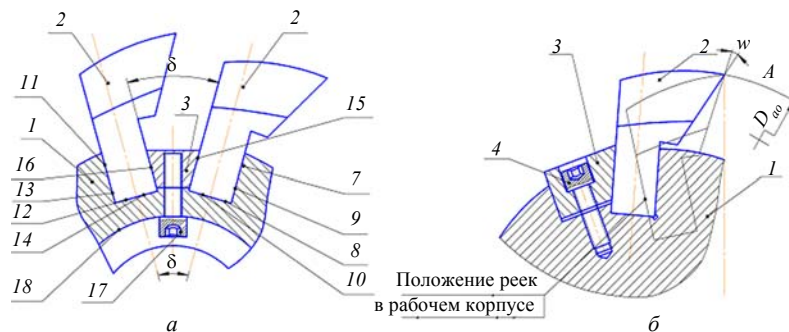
Схема расположения зубчатых реек: а – в рабочем корпусе; б – в технологическом корпусе
